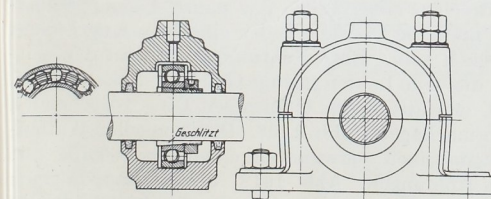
Triebwerk-kugellager von Fichtel und Sachs, Schweinfurt.
